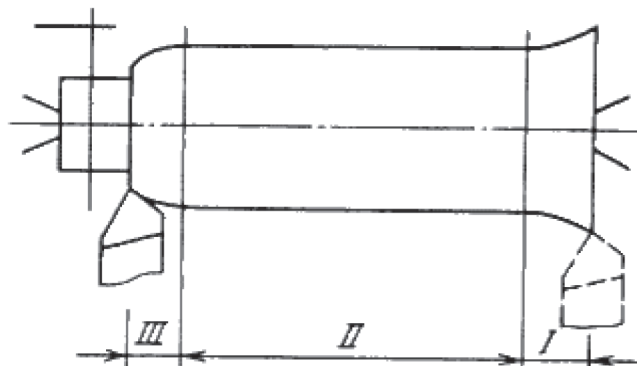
Перекручування форми поверхні деталі під впливом теплового поля: I – ділянка, що утворилася при наростаючому нагріванні заготовки і різця на початку оброблення; II – ділянка, яка виникла при сталому тепловому полі; III – ділянка при погіршенні відведення теплоти наприкінці оброблення
